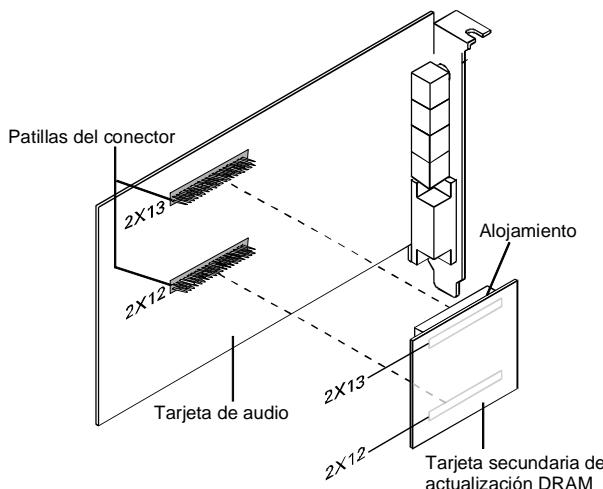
Montaje de tarjeta secundaria de actualización DRAM.
